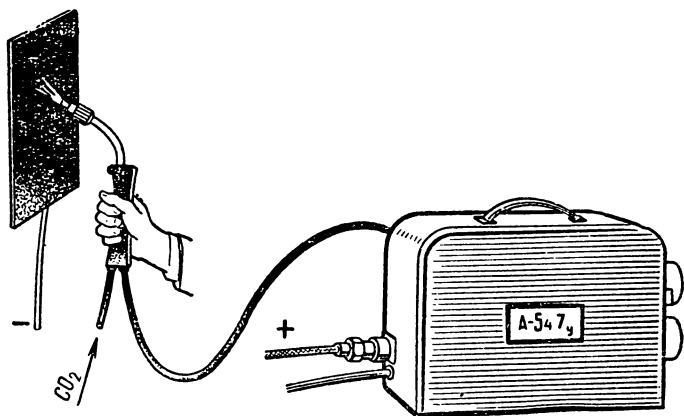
Полуавтомат А-547у для сварки в среде углекислого газа
